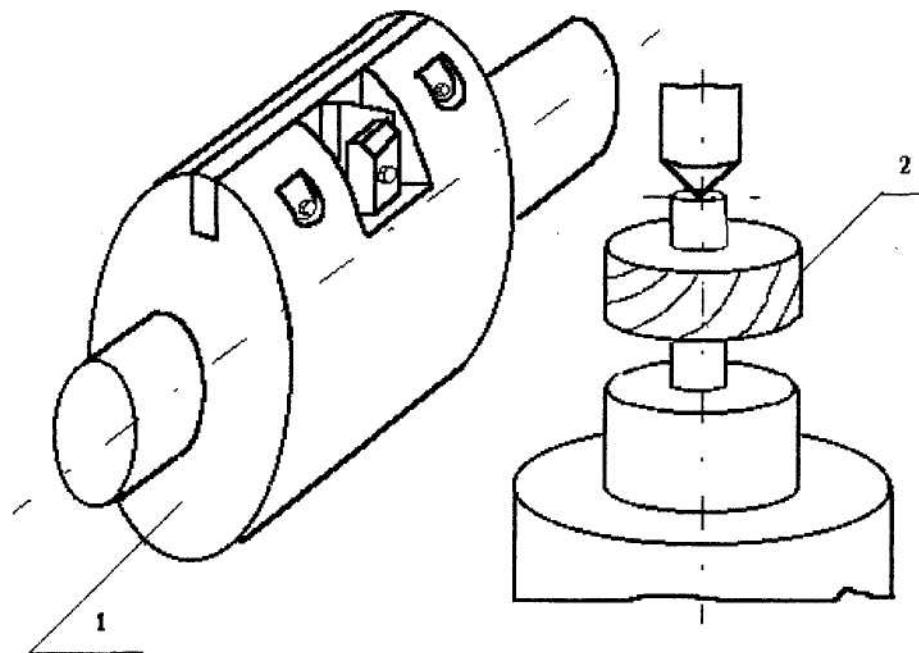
Схема зубофрезерування: 1 – фреза-летучка; 2 – оброблювана деталь
